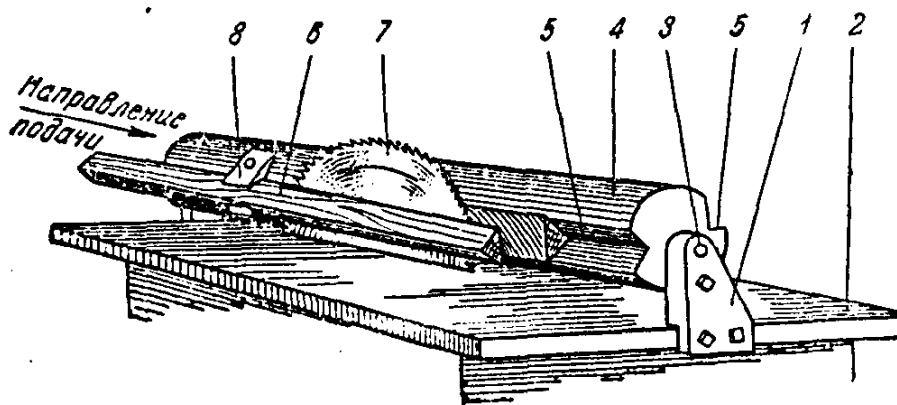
Распиловка заготовки на бобышки треугольной формы.
